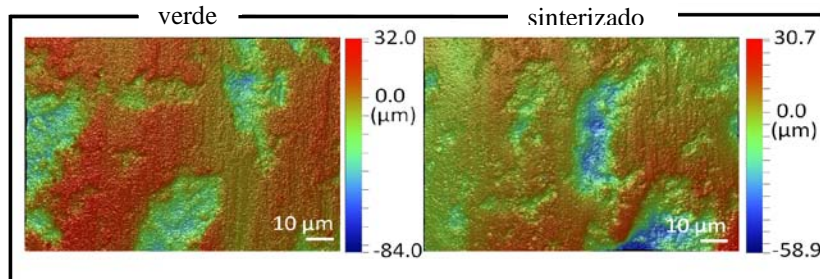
Aspecto da superfície do corpo-de-prova usinado em verde e sinterizado.
